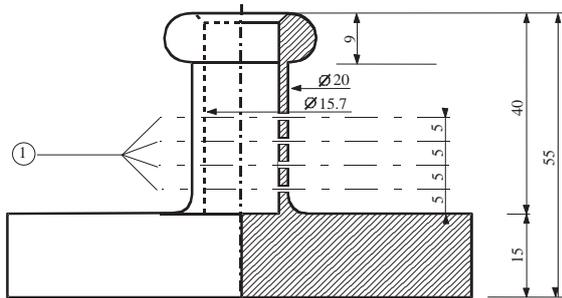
Cylindre creux en bronze, fermé d'un côté ; Plan et coupe verticale, dimensions en mm
